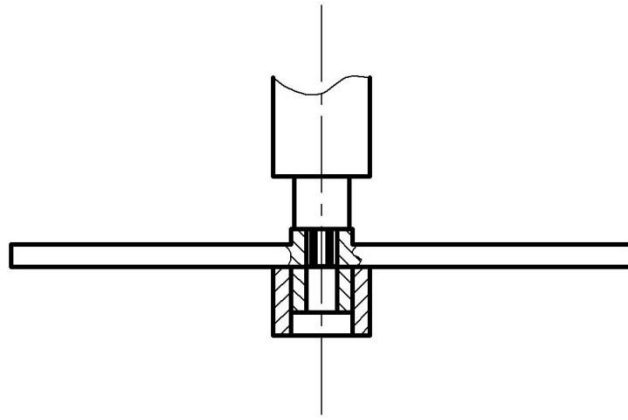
Схема позиции IV «разгрузка» четырехпозиционного роторного сборочного автомата 5
